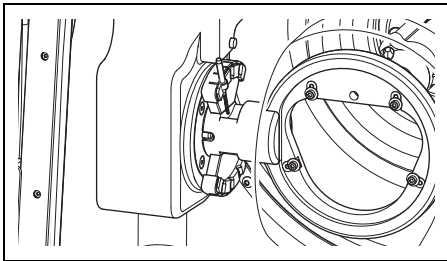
Werkzeughalter (Fünf-Achs-Modell)
